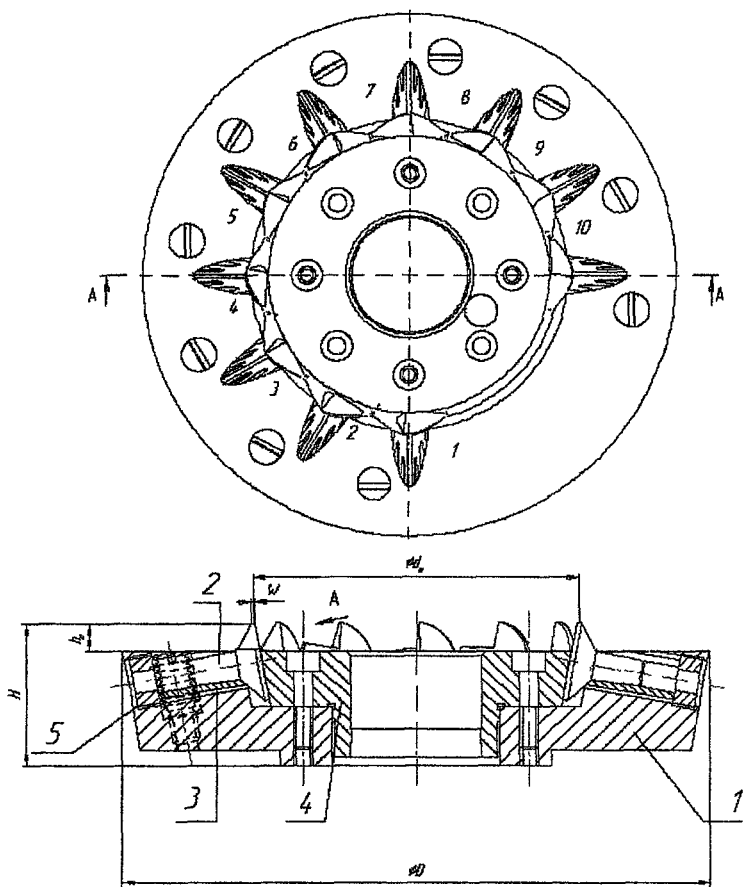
Общий вид зуборезной головки-протяжки с круглыми резами
